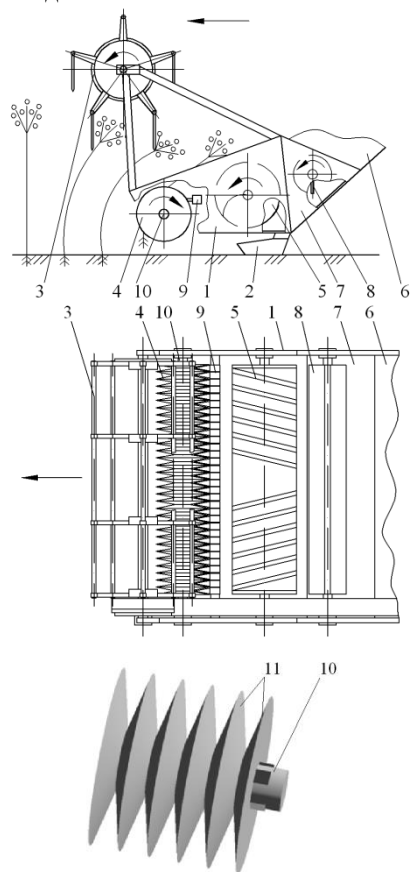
Зернозбиральний комбайн оснащений конічно-дисковим льонобральним апаратом: 1 – платформа; 2 – копіювальний пристрій; 3 – мотовило; 4 – бральний апарат; 5 – збірний шнек; 6 – похила камера; 7 – приставка; 8 – бітер; 9 – очисна планка; 10 – приводний вал зі шліцями; 11 – конічні диски
